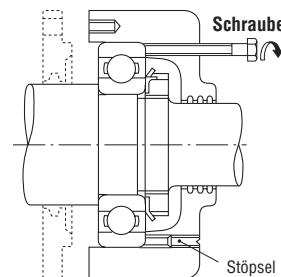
Demontage des Außenrings mittels Schrauben
